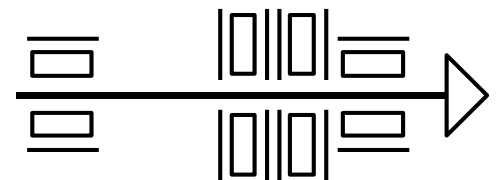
Компоновка ШВ токарного верстата (тандем-О).
